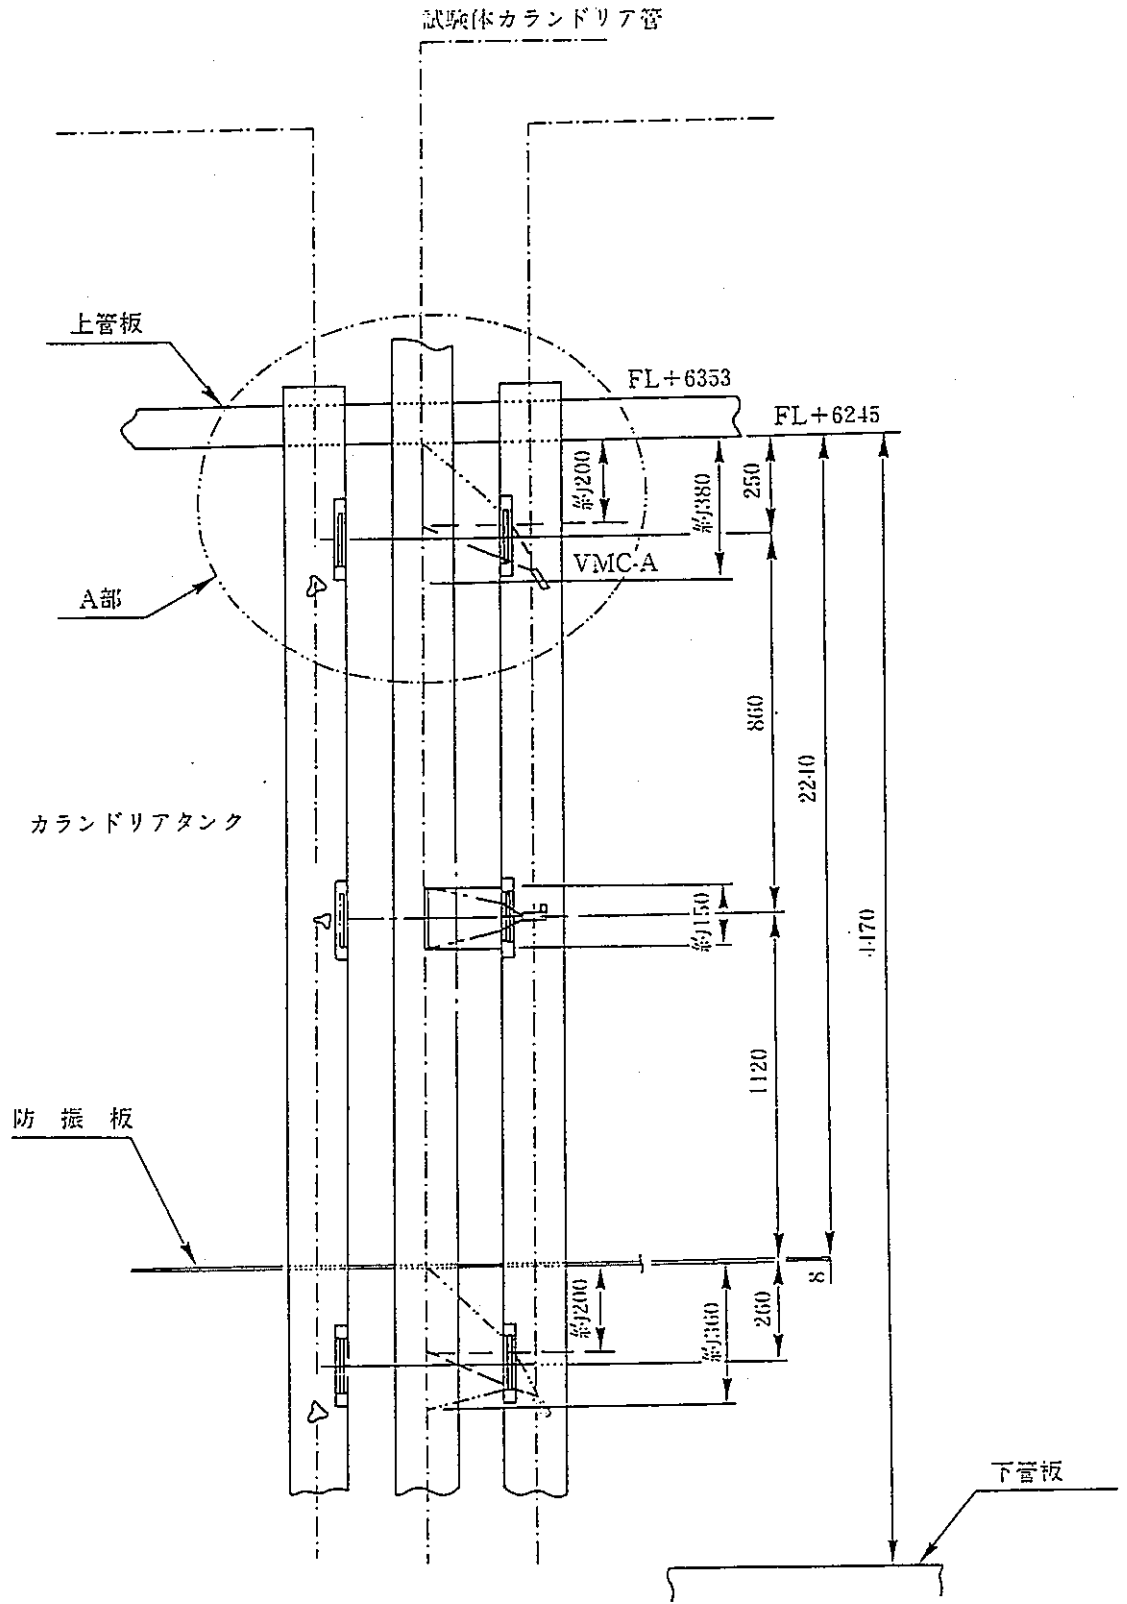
1. 2-10 ボイドモニターカメラ立面配置図
